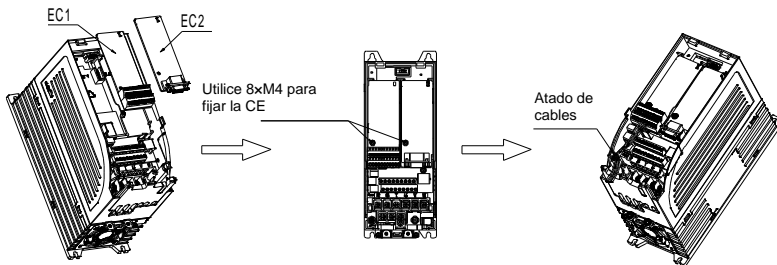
VFD de 1,5-7,5 kW con tarjetas de expansión instaladas
